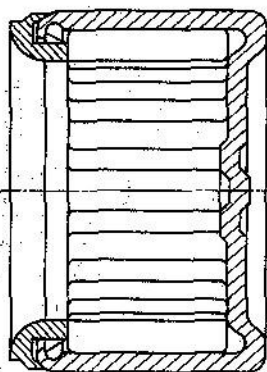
Подшипник крестовины кардана производства фирмы СКФ для легковых автомобилей с корпусом, получаемым без снятия стружки. Доннышко, с которым контактирует торец шипа крестовины, имеет «вафельную» сетку, которая смягчает толчки и одновременно служит для удержания смазочного материала. Иголки прижимаются к доннышку внешним уплотнением. Подшипник устанавливается в вилке с таким натягом, что усилие выпрессовки составляет не менее 1 кН; для дополнительного стопорения корпуса подшипника служит зачеканивание вилки в 4—6 местах равномерности вращения. Из-за высокой частоты вращения (6000 мин^{-1} и более) уплотнительный чехол 4 помещен внутрь колпака 3 из стального листа (рис. 2.103), к которому он прижимается под действием центробежной силы. На этом рисунке показаны возможная величина смещения шарика от положения 1 до положения 2 и центрирование по перифе-
